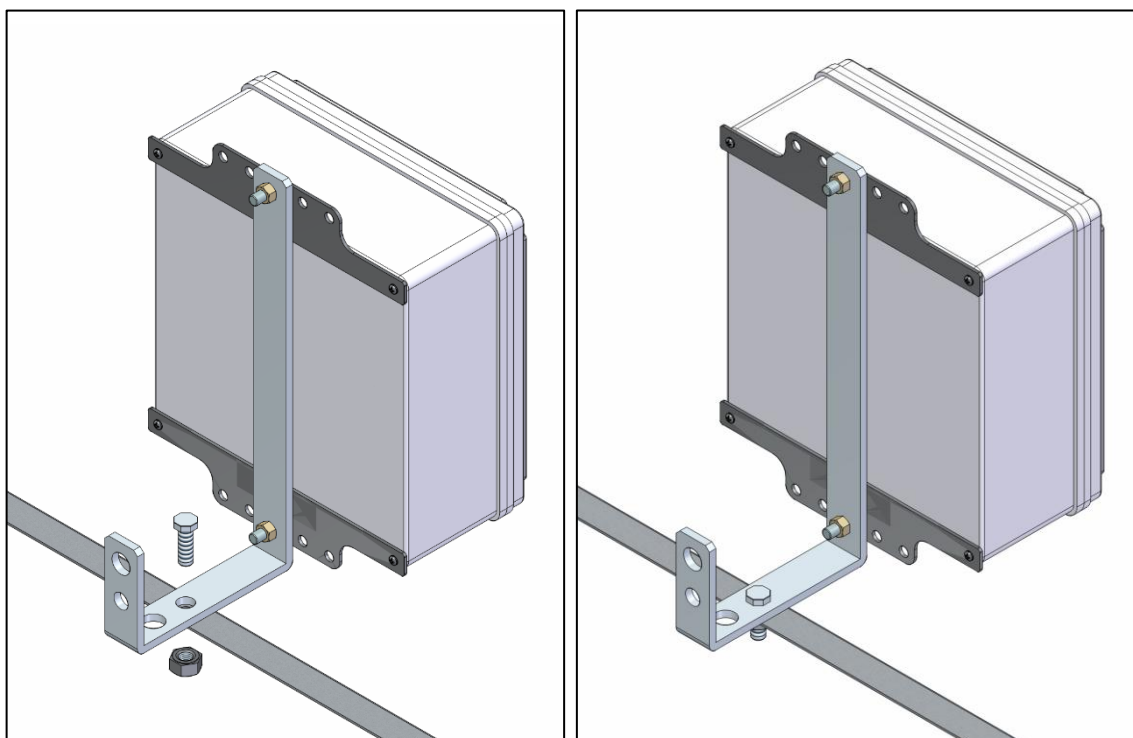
Fixação do GPS CAN na face superior da viga do pivô.
